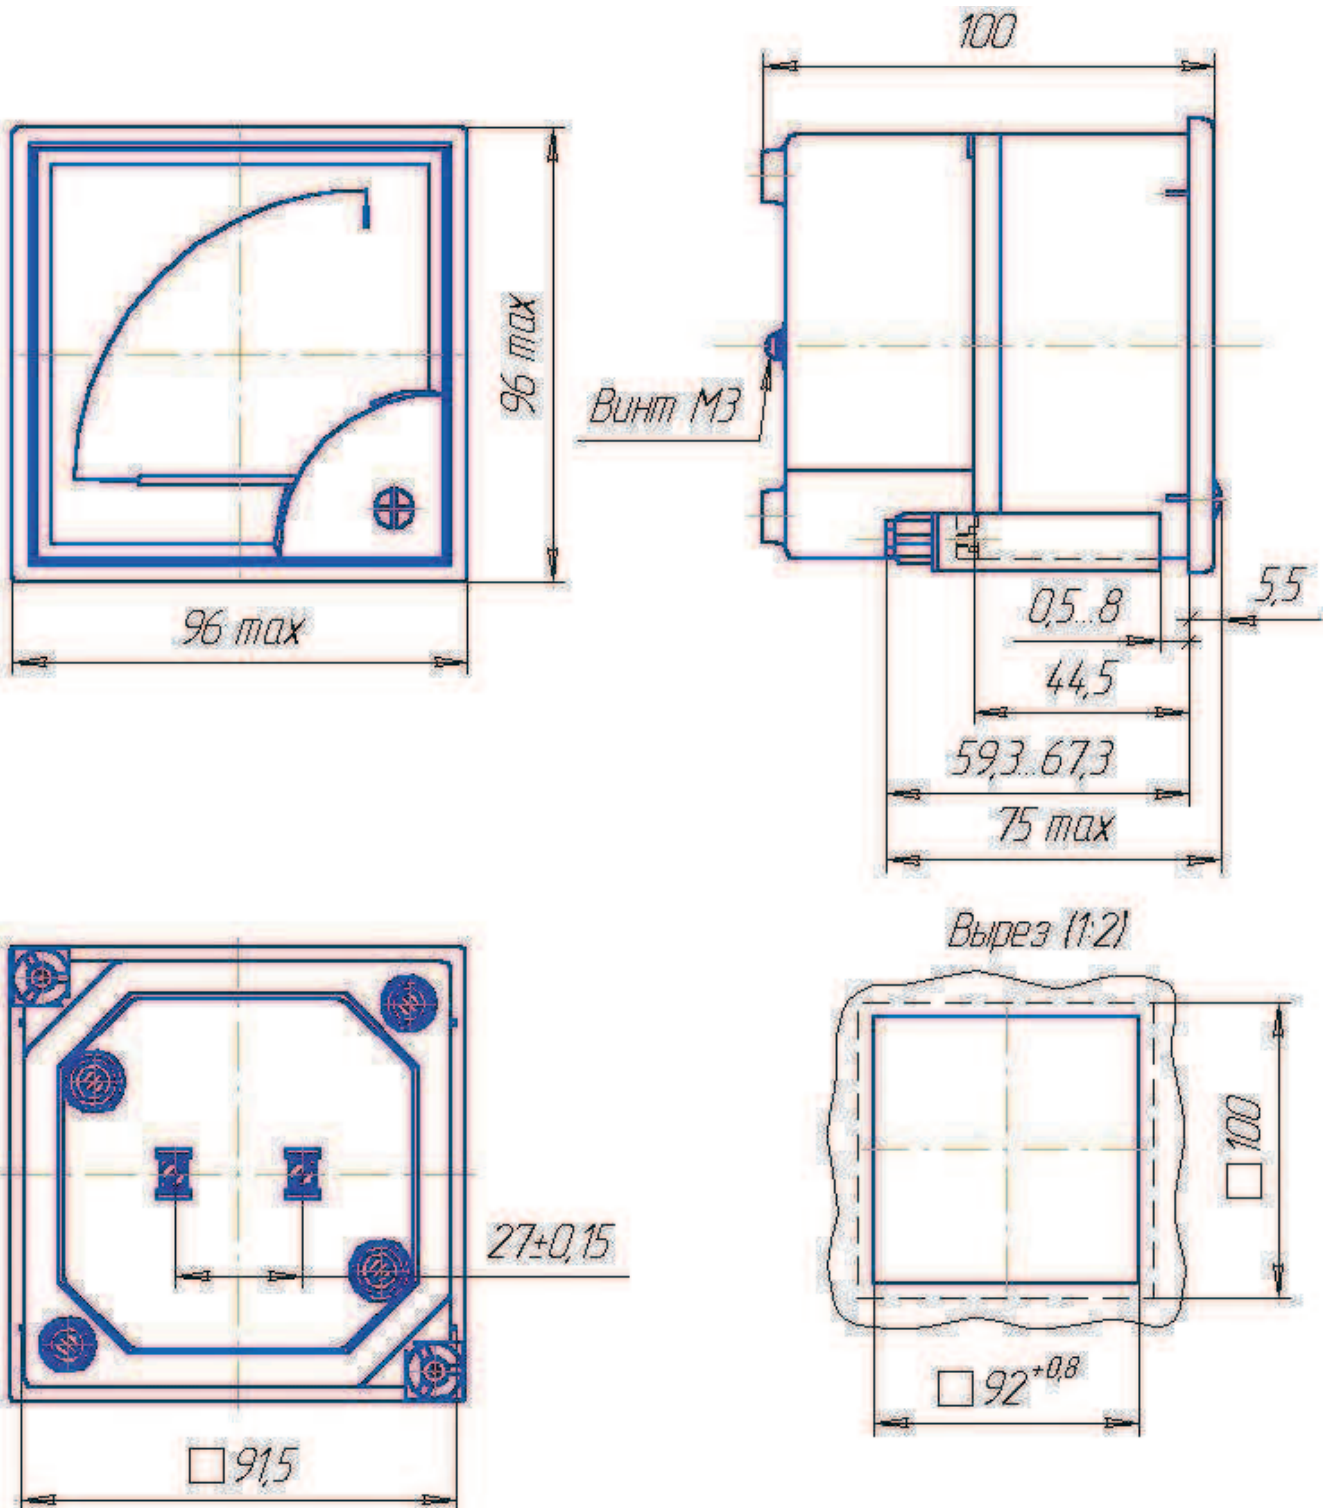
Габаритные размеры частотомера Ц42306
